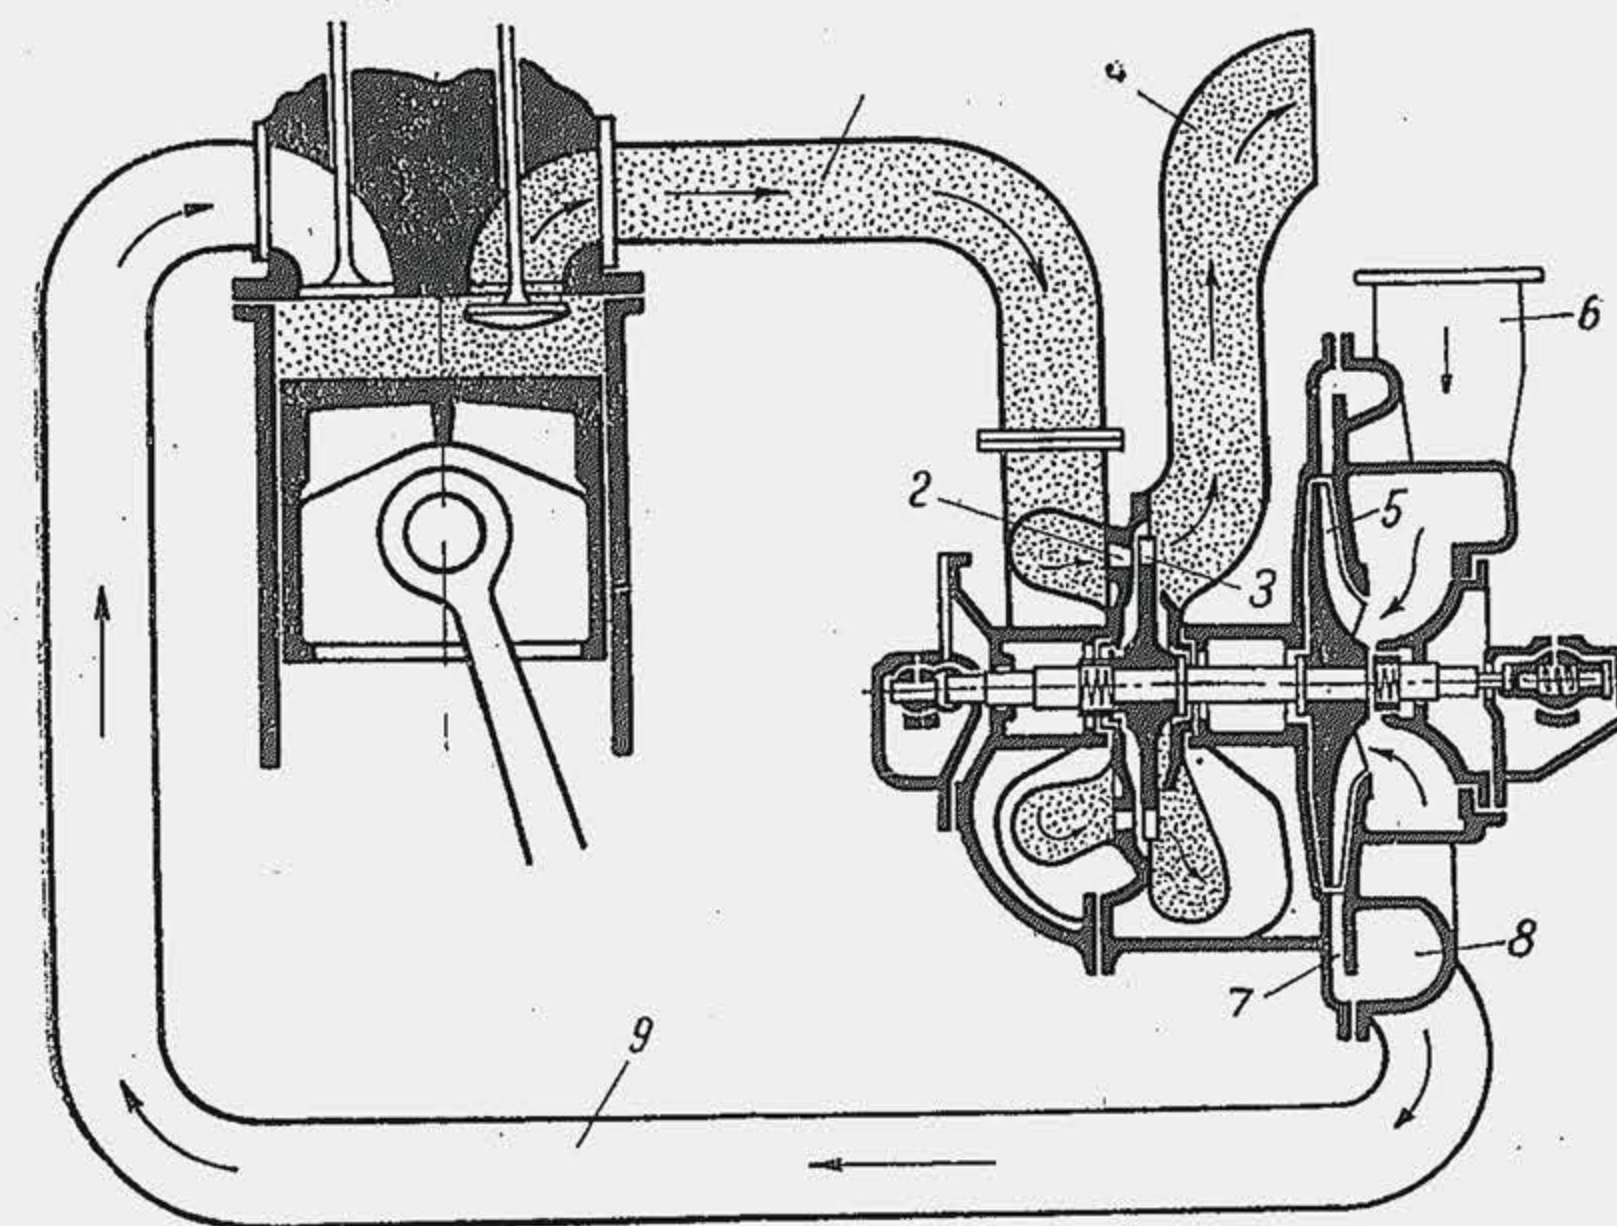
Schema supraalimentării prin turbosufiantă; 1 — axul de rotație; 2 — ajutajele turbinei; 3 — rotorul turbinei; 4 — conductă de evacuare; 5 — rotorul suflantei; 6 — racord de admisiune; 7 — difuzor; 8 — melc de refulare; 9 — conductă de refulare.
